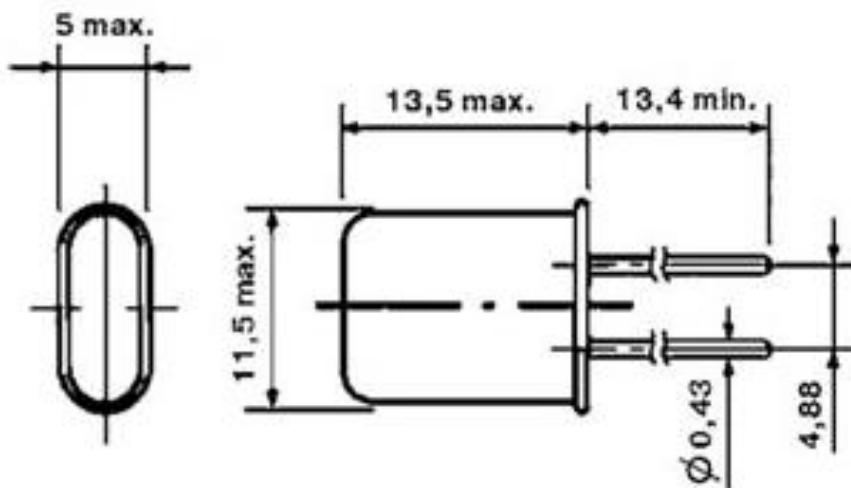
Габаритні розміри кварцового резонатора НС-49U
